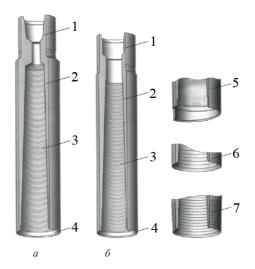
Колокол: a — несквозной типа ЛК; δ — сквозной типа ЛКС; 1 — резьба присоединительная; 2 — корпус колокола; 3 — резьба ловильная; 4 — воронка с фаской; 5 — воронка с вырезом; δ — фаска; 7 — резьба под направление
